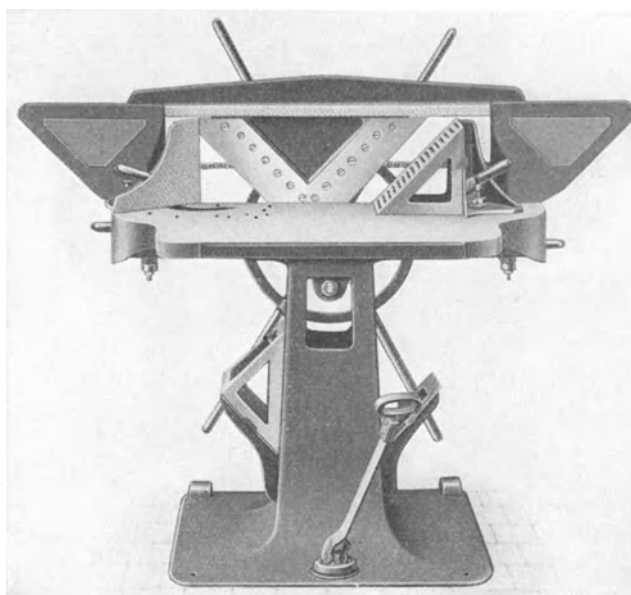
Fahrbare Universal-Gehrungsbestoßmaschine.
